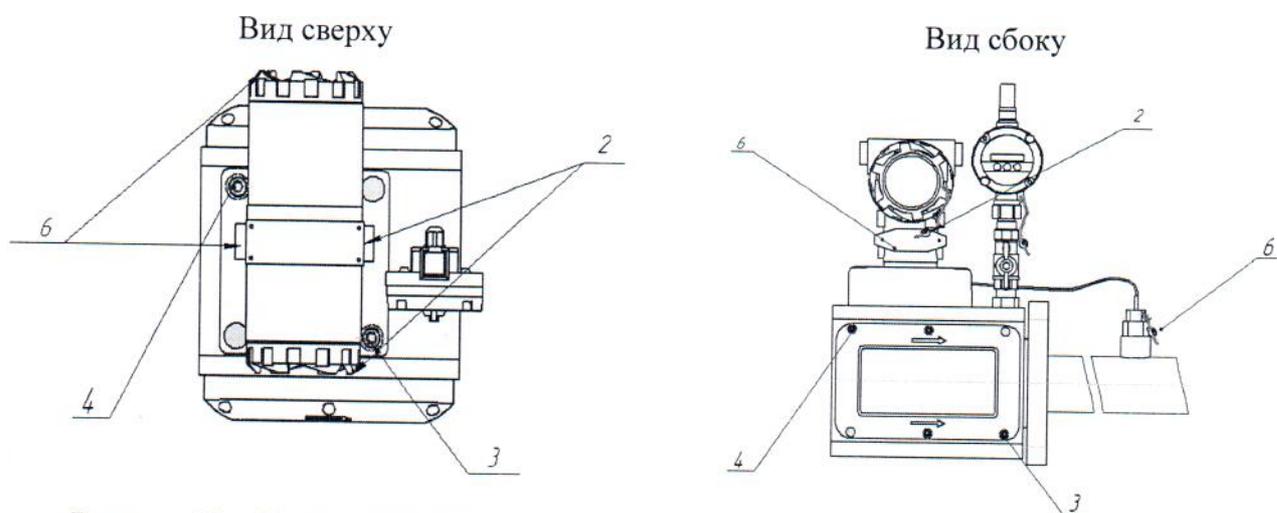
Корпус прямоугольного сечения с совмещенными защитными крышками
